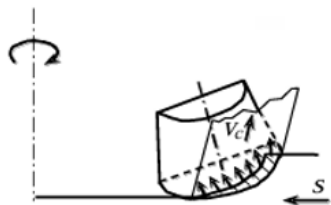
Напрямок сходу стружки при торцевому фрезеруванні ножами з конічною передньою та плоскою задньою поверхнями
